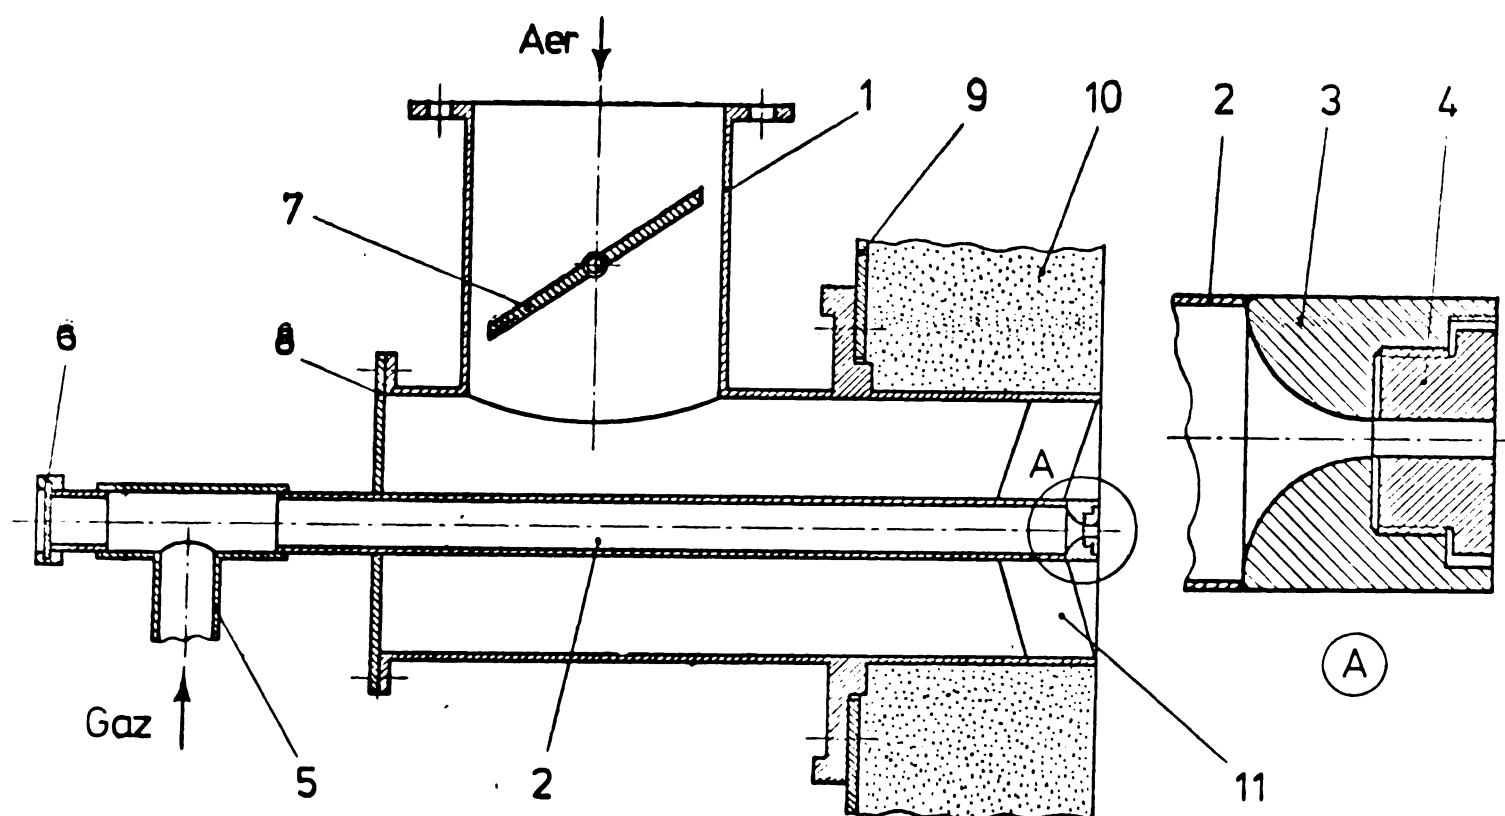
Schema de montaj a arzătorului experimental pe placa frontală a focarului.
